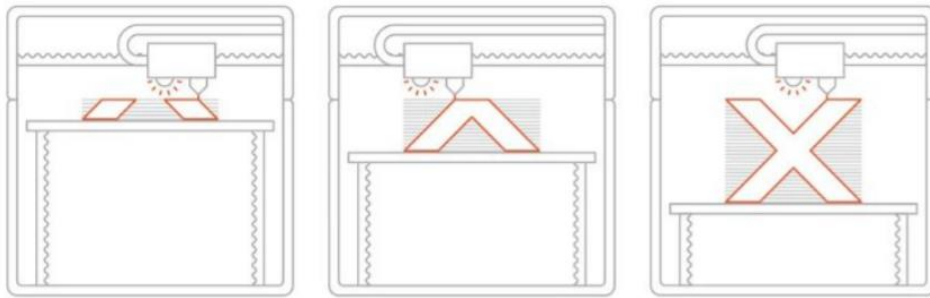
Processo de impressão 3D - PolyJet ou Material Jetting
